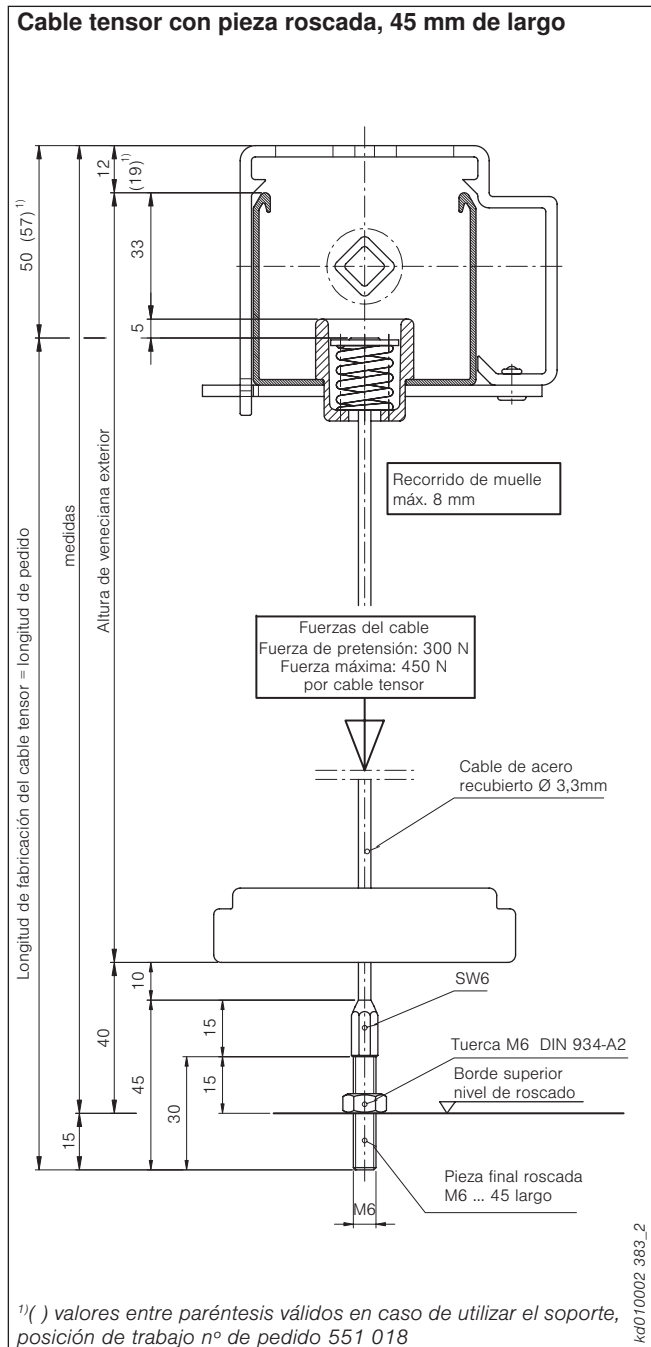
Cable tensor con pieza final roscada, 45 mm de largo
